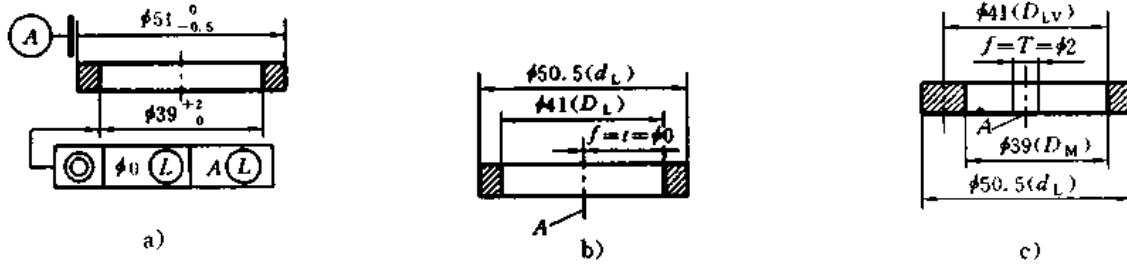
同轴度公差采用最小实体要求的零形位公差
